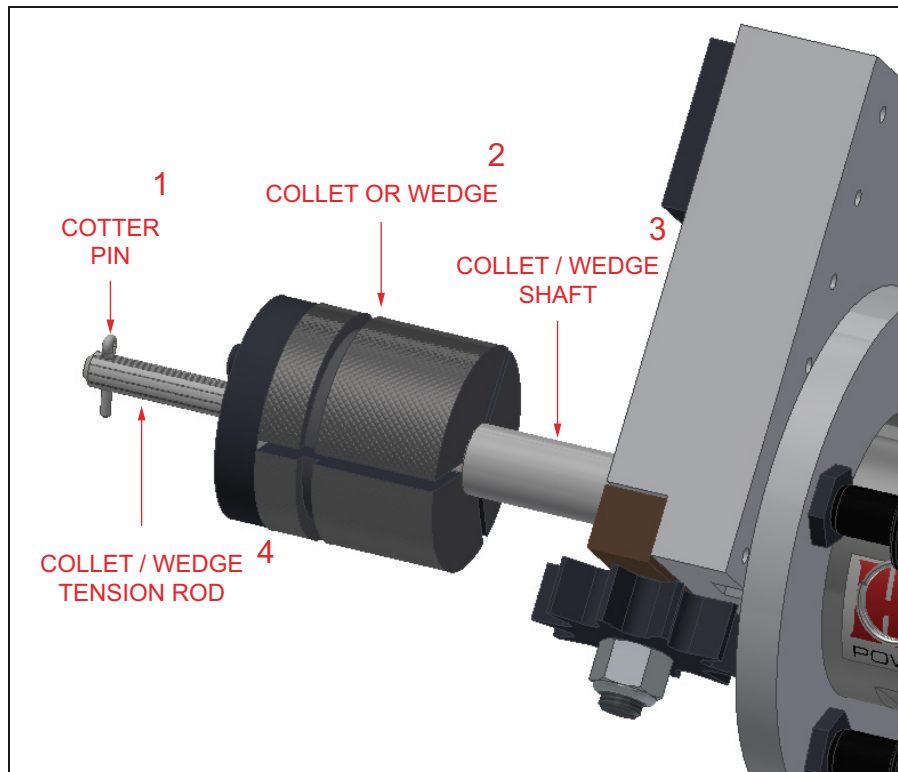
PASADOR DE CHAVETA Y OTROS COMPONENTES DE LA BOQUILLA/CUÑA
